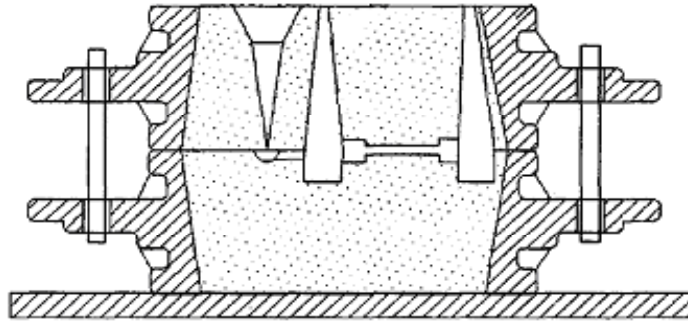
Схема ливарної форми для одержання зразків
